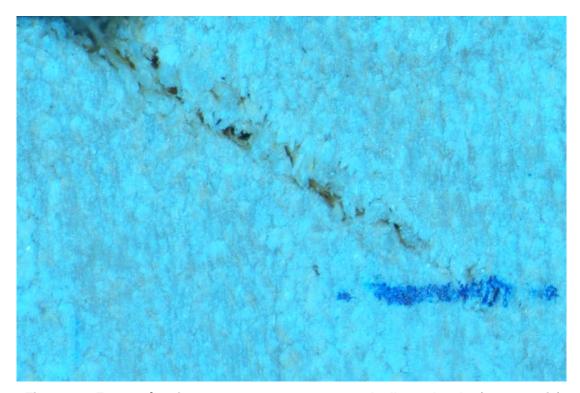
Fente mécanique sur une coupe transversale d'une planche (vue grossie)
